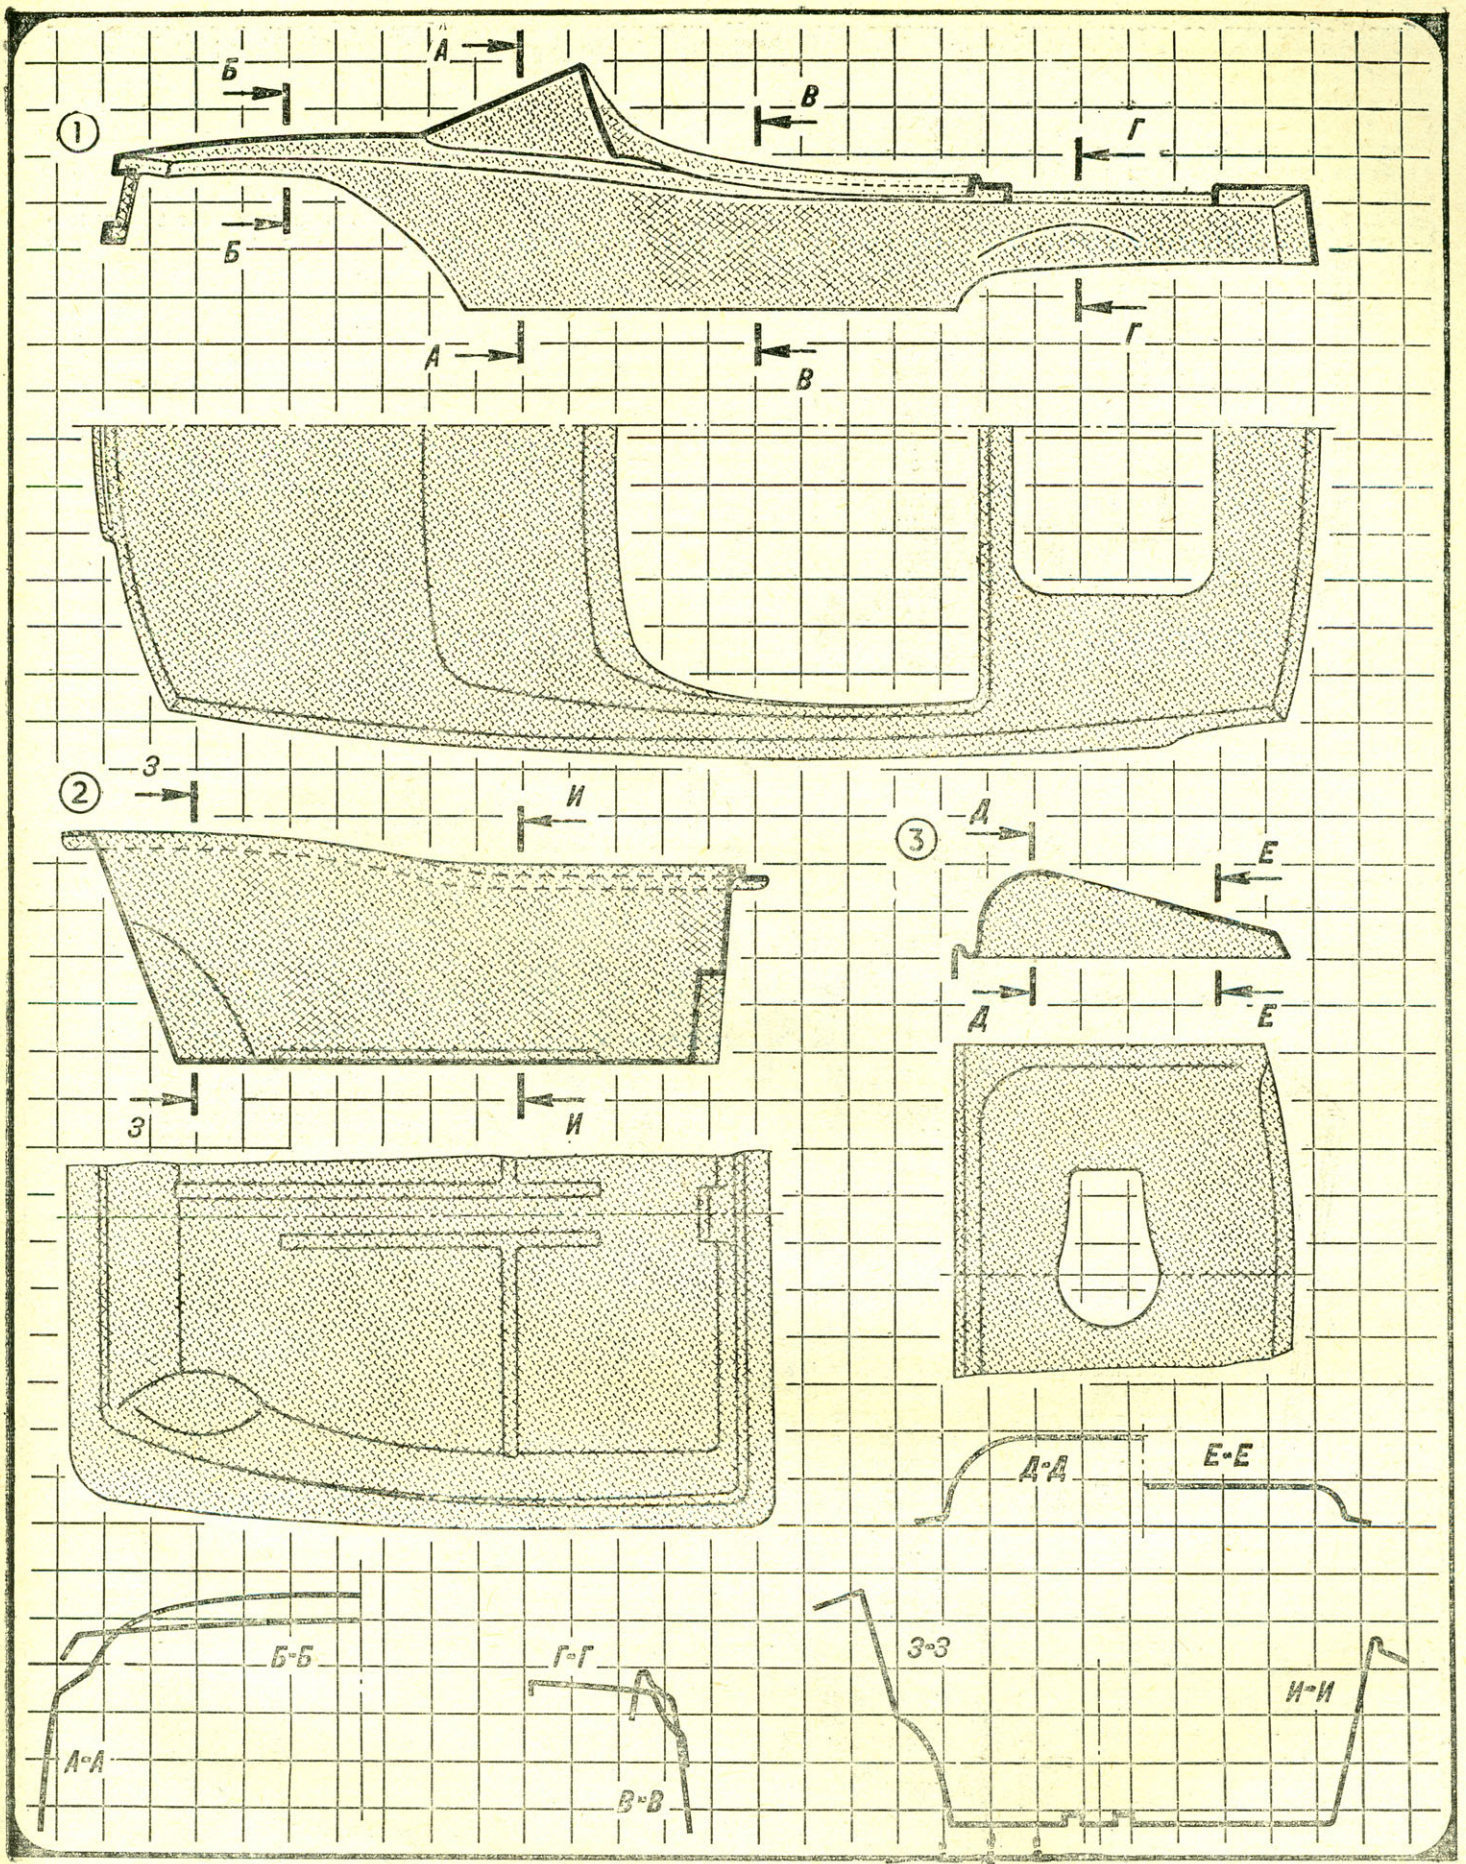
Элементы стеклопластикового кузова: 1 — верхняя часть корпуса, 2 — нижняя часть, 3 — полукapot двигателя.
